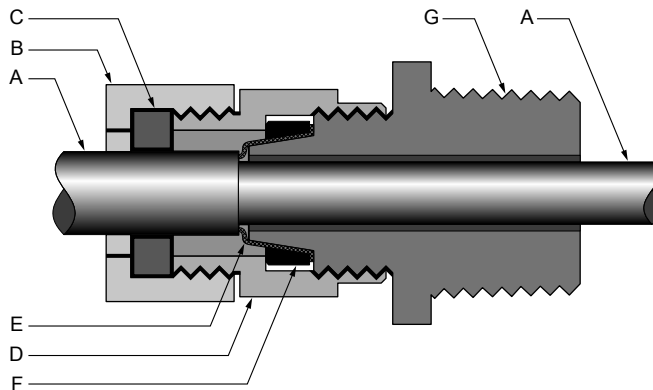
Presse-étoupe et câble (vue éclatée)
